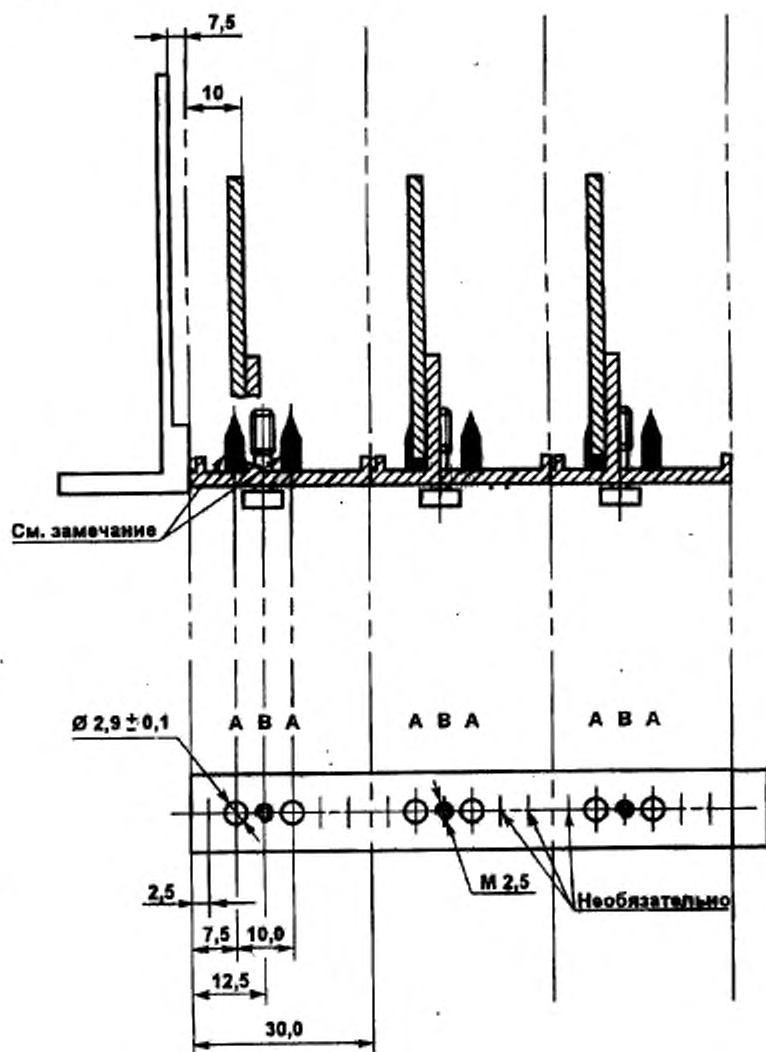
3 — Вид крейта с контрольными размерами для нижней части установленного разъема
